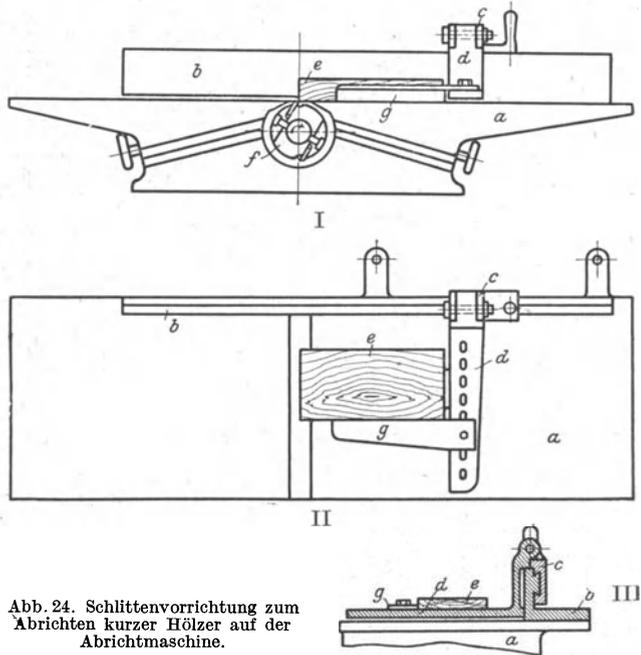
Schlittenvorrichtung zum Abrichten kurzer Hölzer auf der Abrichtmaschine.
